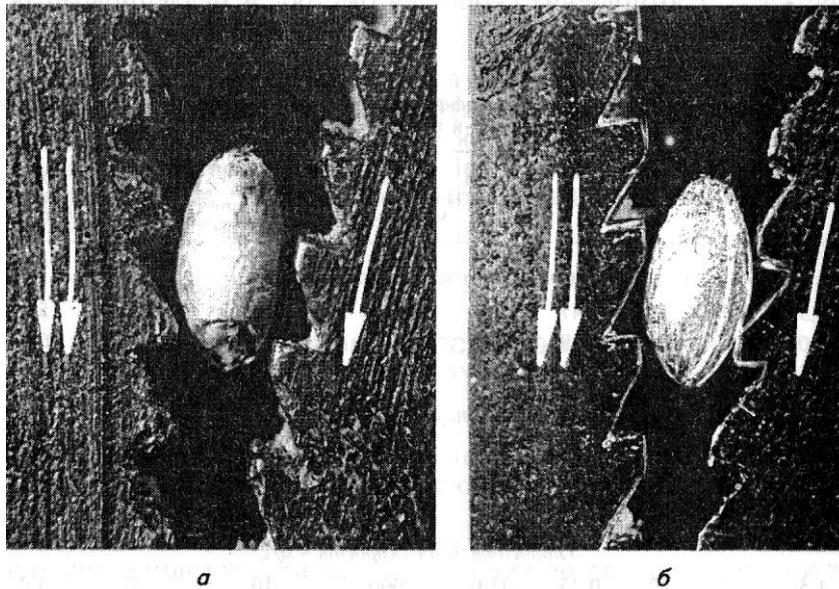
Форма (а) и профиль (б) рифлей вальцового станка
